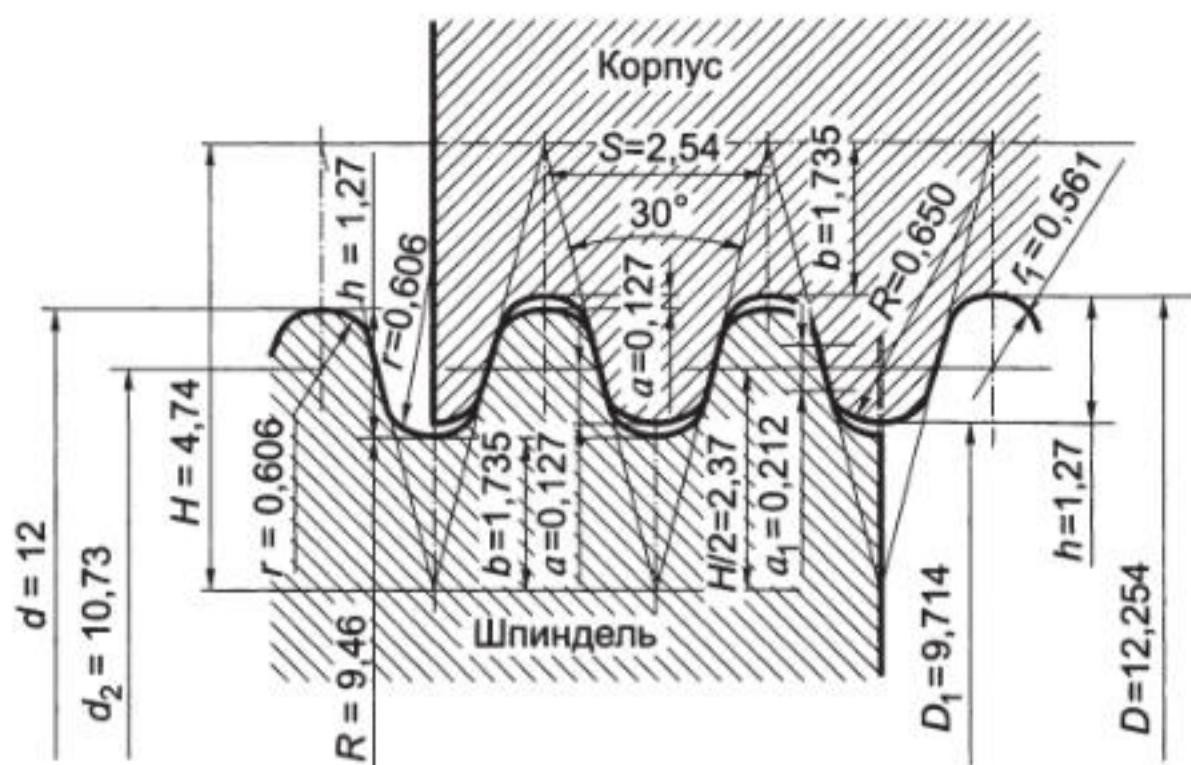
Профиль и размеры круглой резьбы санитарно-технической арматуры
